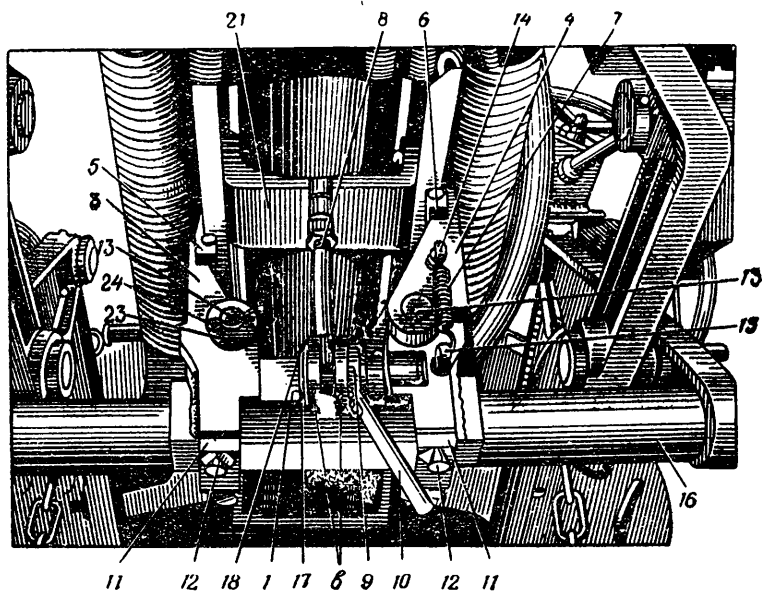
Приспособление для крепления качающейся части миномета по-походному новой конструкции (СБ15) (вид спереди):
